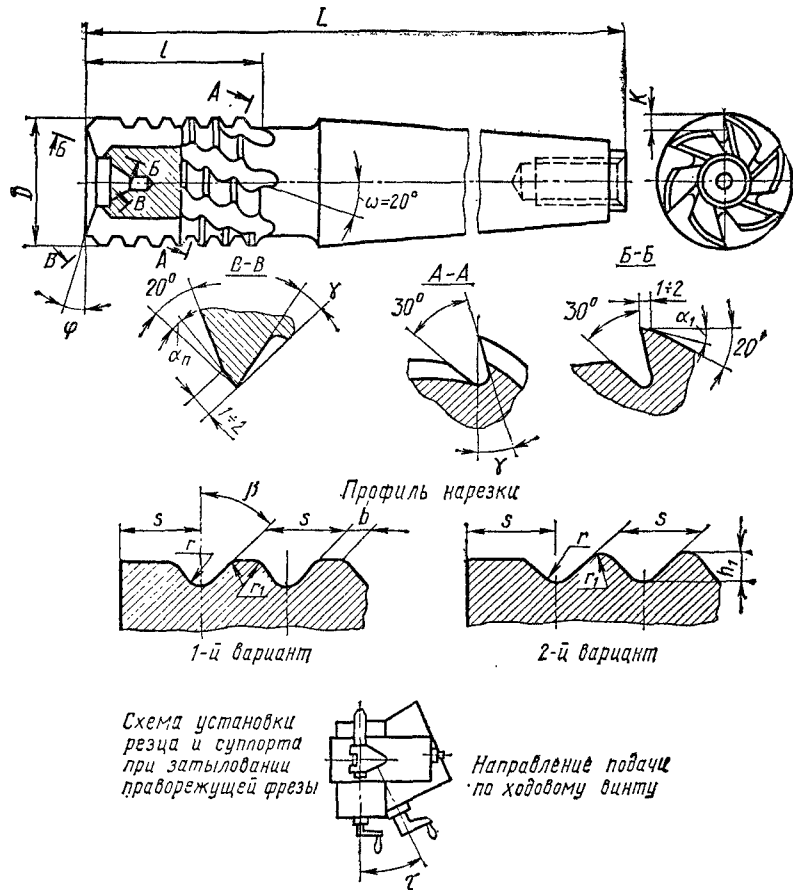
Цилиндрическая фреза с затылованными зубьями («кукурузная»)
